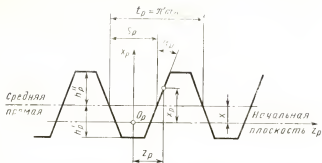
Параметры профиля инструментальной рейки для эвольвентных зубчатых колес
